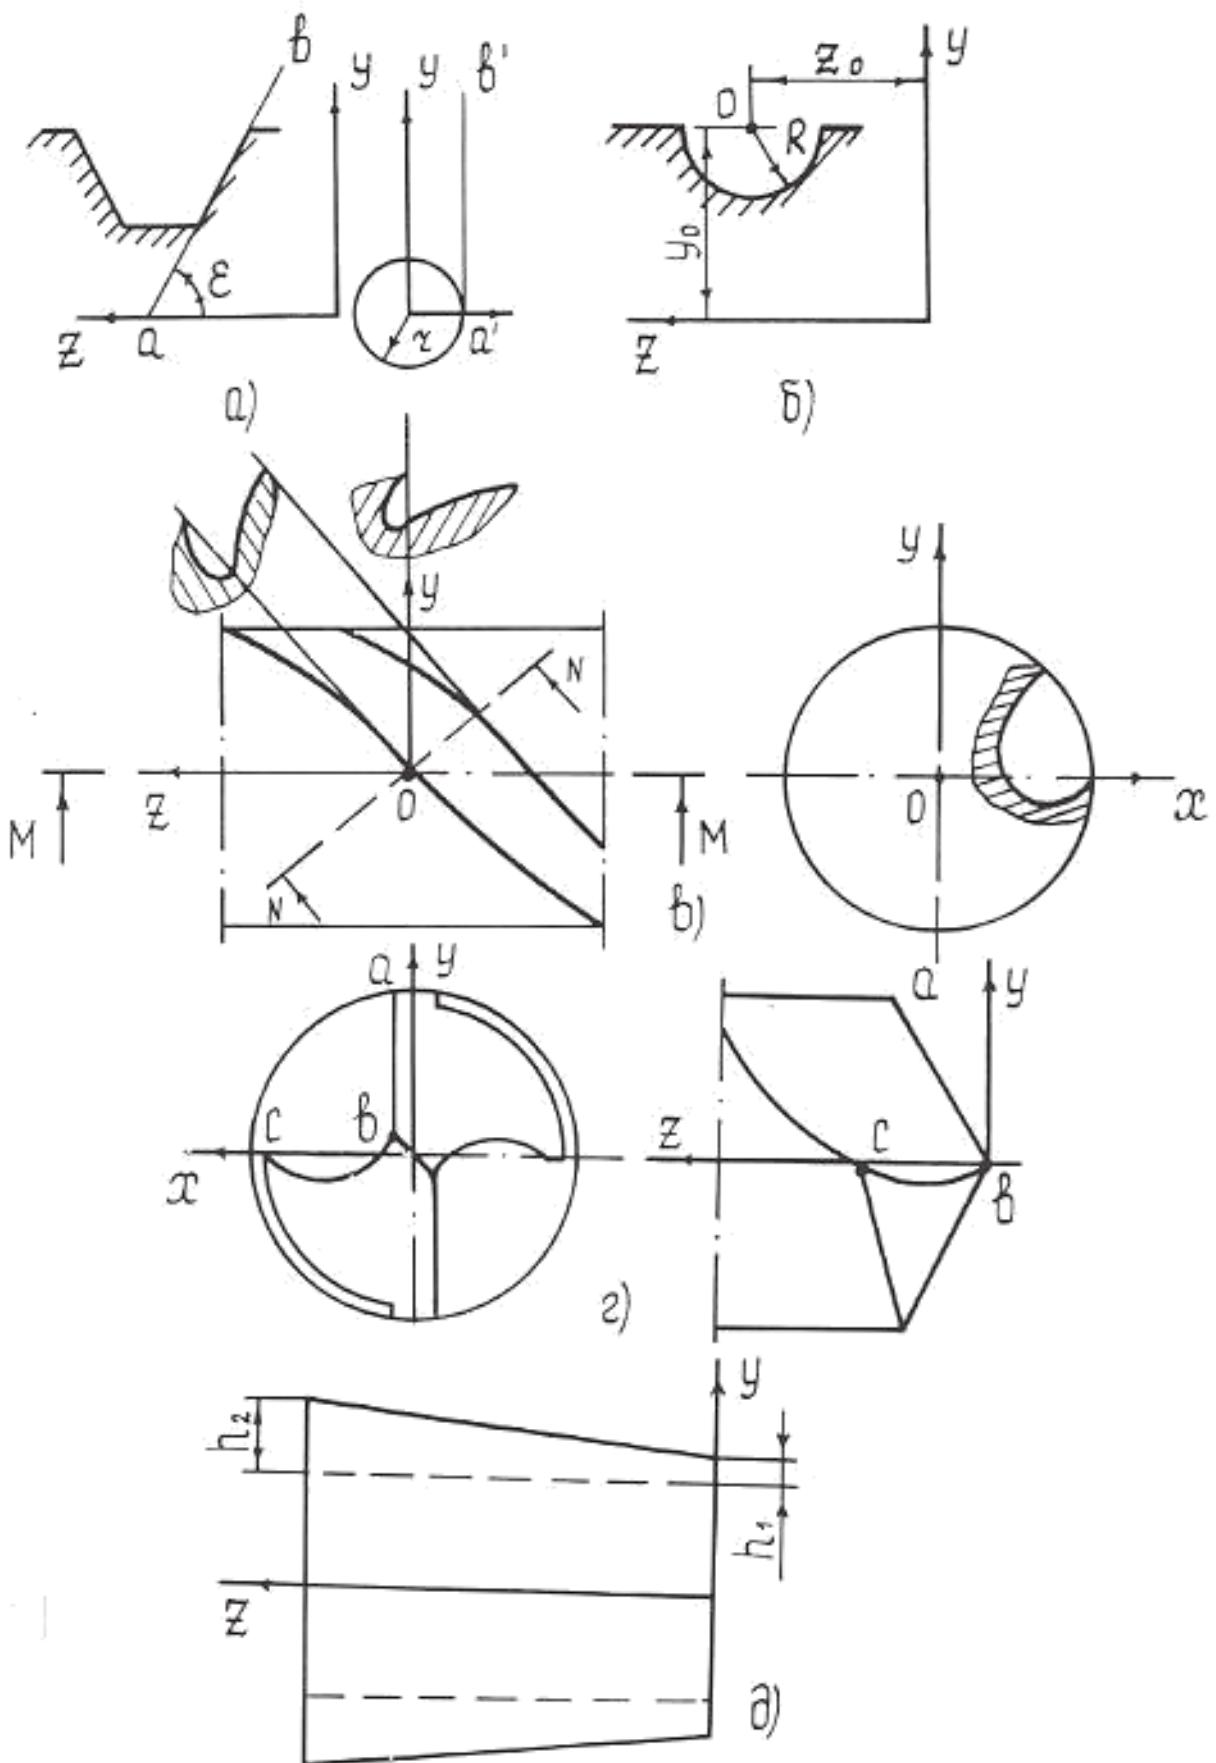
Виды винтовых поверхностей режущего инструмента
